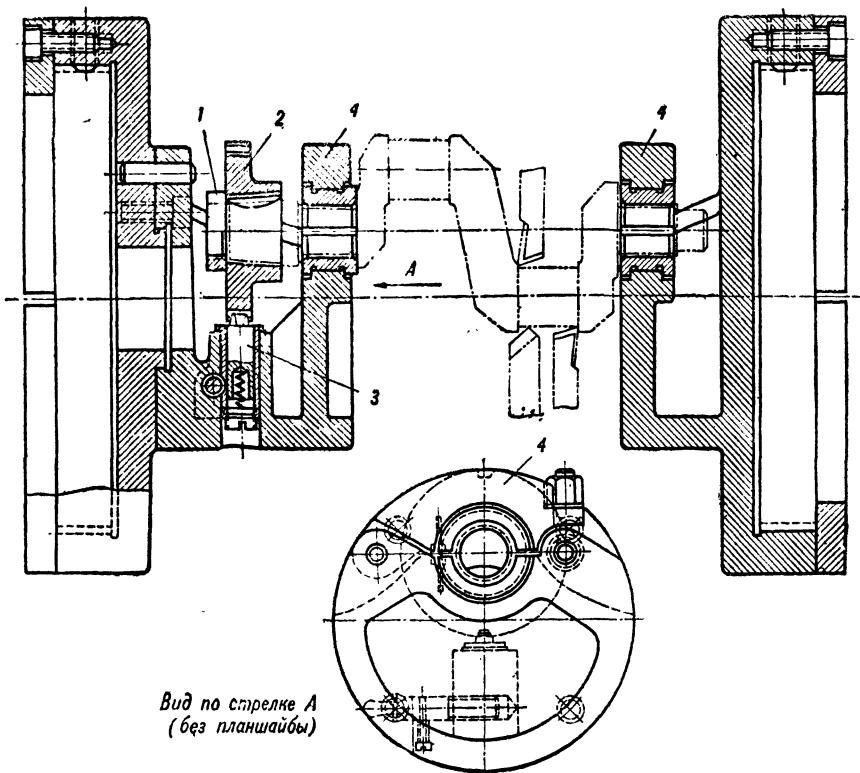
Приспособление для обработки шатунных шеек коленчатого вала.
